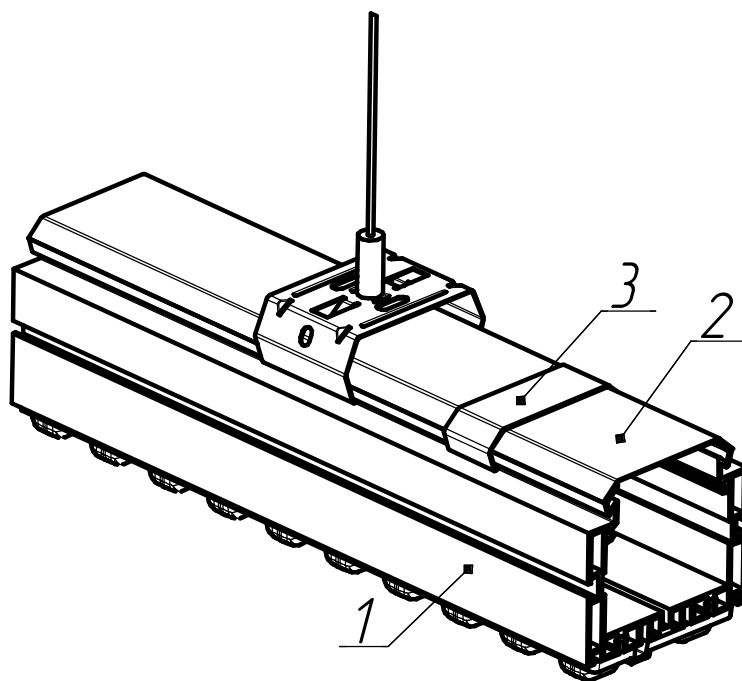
Светильник с защитной крышкой корпуса,
